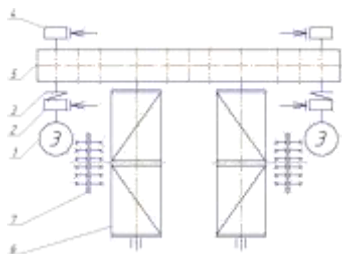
Конструкция с шестеренчатым редуктором (схема №4)
